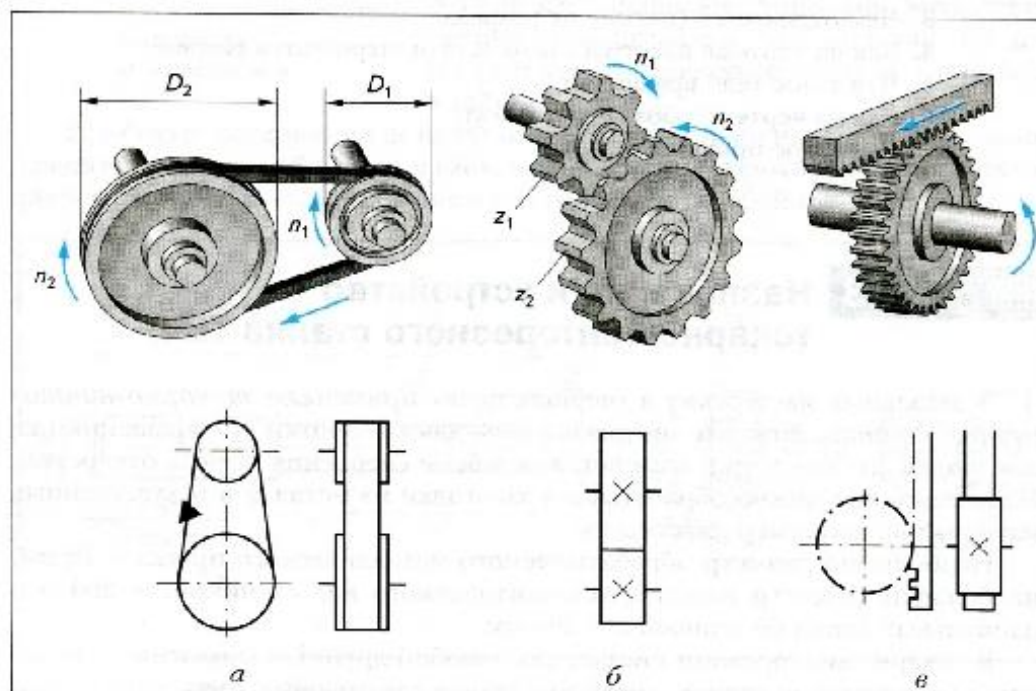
Виды механических передач, применяемых в токарном станке, и их условные обозначения: а — ремённая; б — зубчатая; в — реечная
